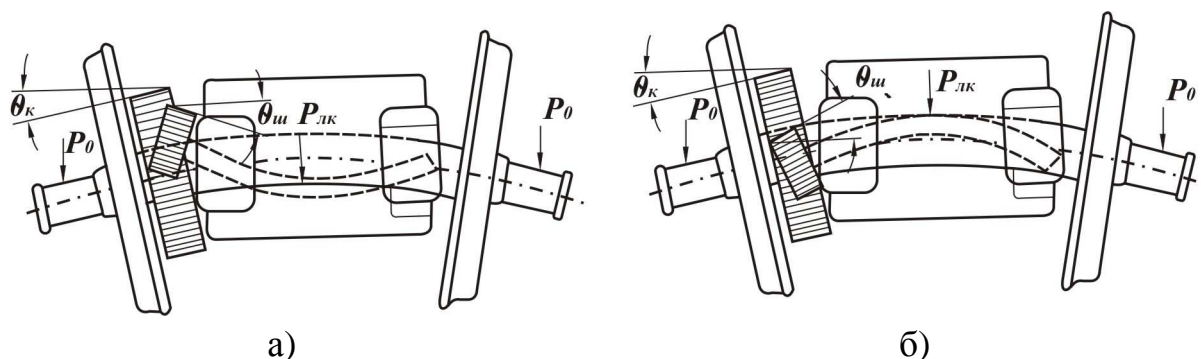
Расчетные схемы взаимного положения шестерни и зубчатого колеса тяговой передачи в режиме тяги
